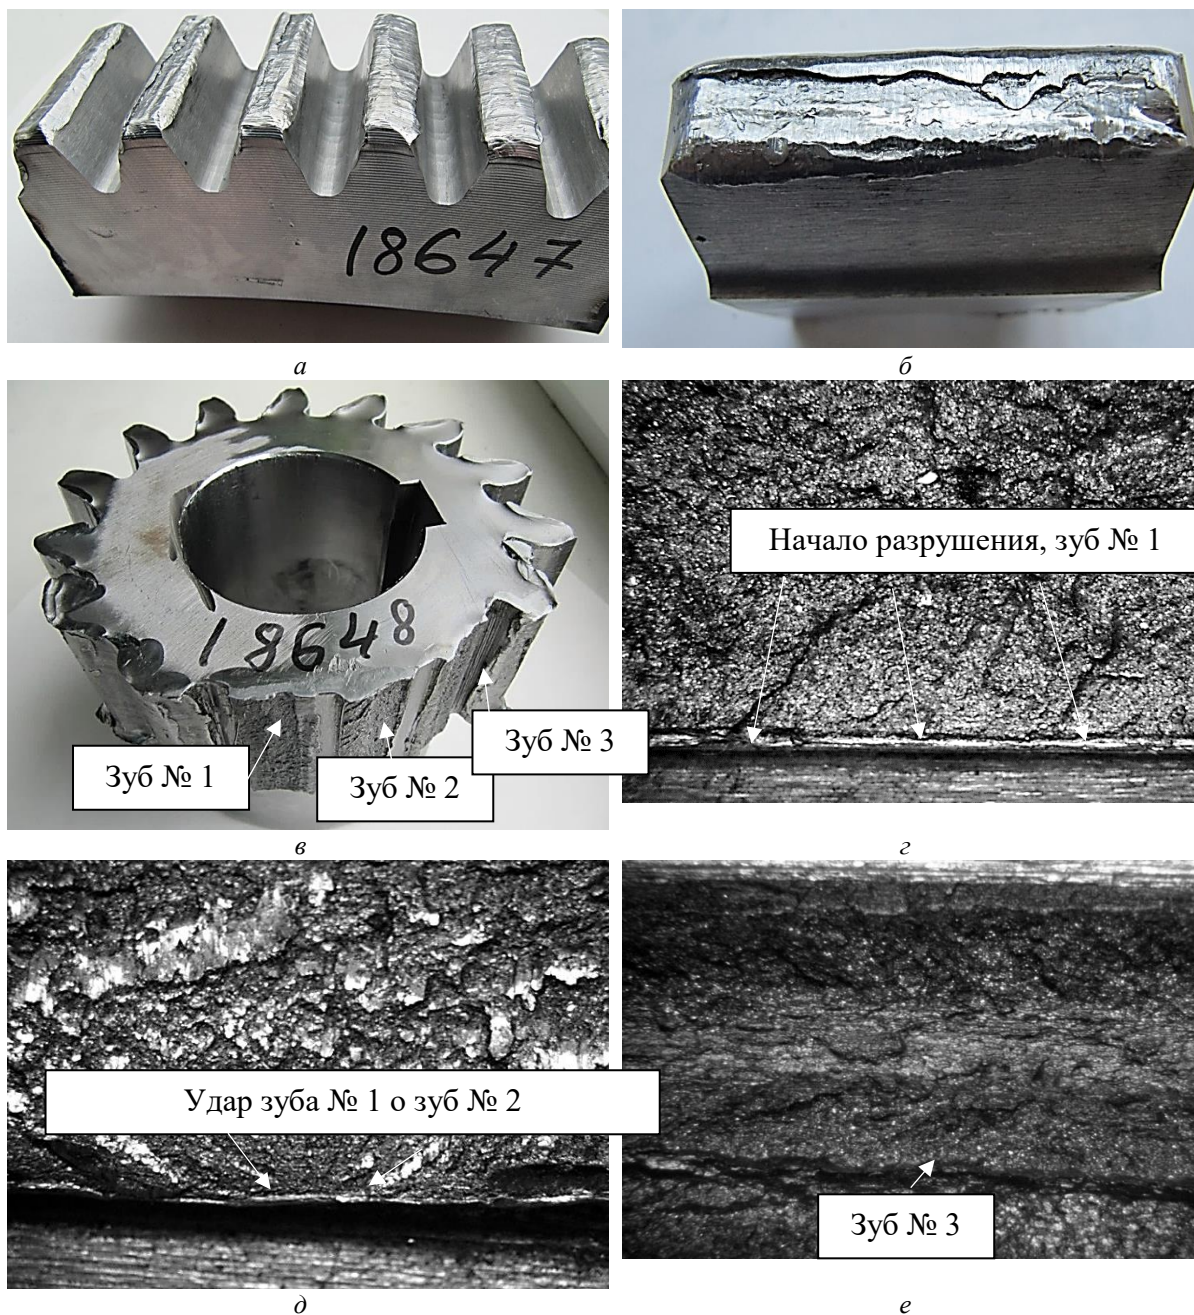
Венец и шестерня: а – общий вид венца; б – смятый зуб венца; в – общий вид шестерни; г – морфология излома под разрушенным зубом № 1 шестерни (множественные очаги); д – морфология излома под разрушенным зубом № 2 шестерни (очаг удара зуба № 1 о зуб № 2); е – морфология излома зуба № 3 (катастрофическое разрушение)
